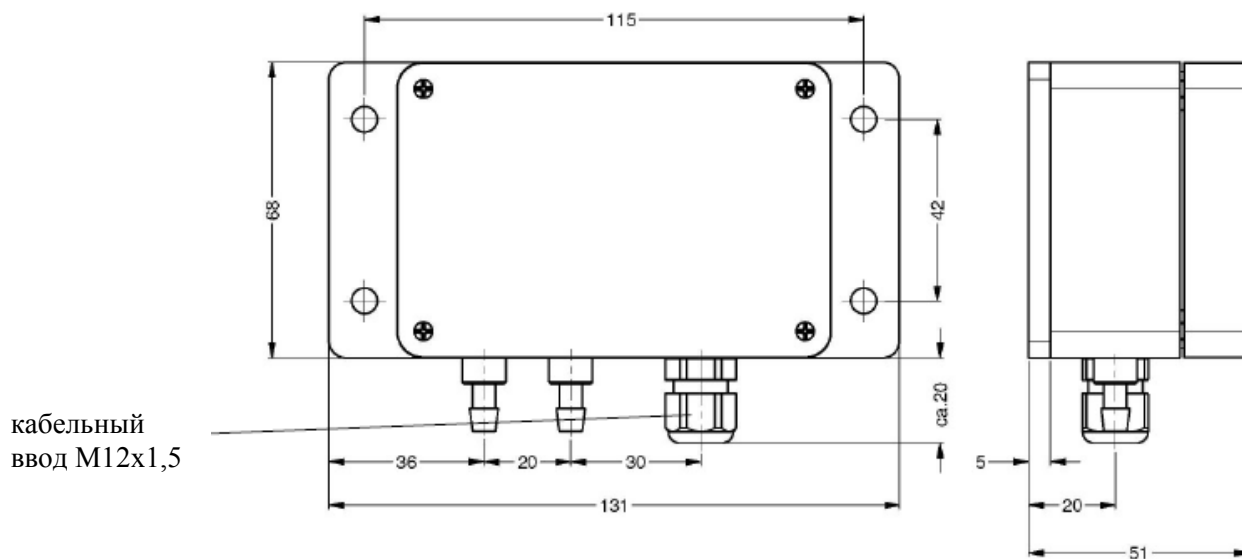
Габаритные и присоединительные размеры датчика без индикатора.
